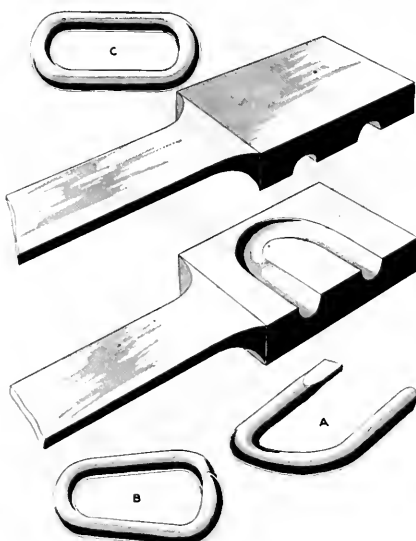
SOLDADURA DE UN ESLABÓN HECHA A TROQUEL
